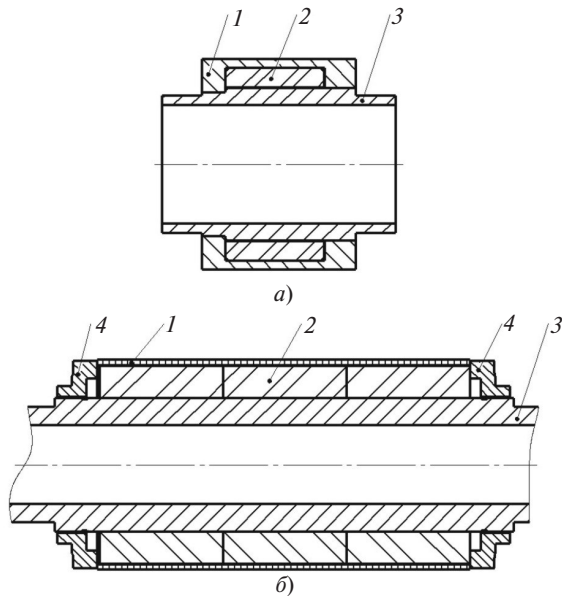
Конструктивные схемы ротора с радиально намагниченными постоянными магнитами и немагнитной обоймой: *a* – схема с массивной обоймой; *б* – схема с шихтованной обоймой; 1 – немагнитная обойма; 2 – постоянный магнит; 3 – вал (ядро индуктора); 4 – стягивающая гайка
